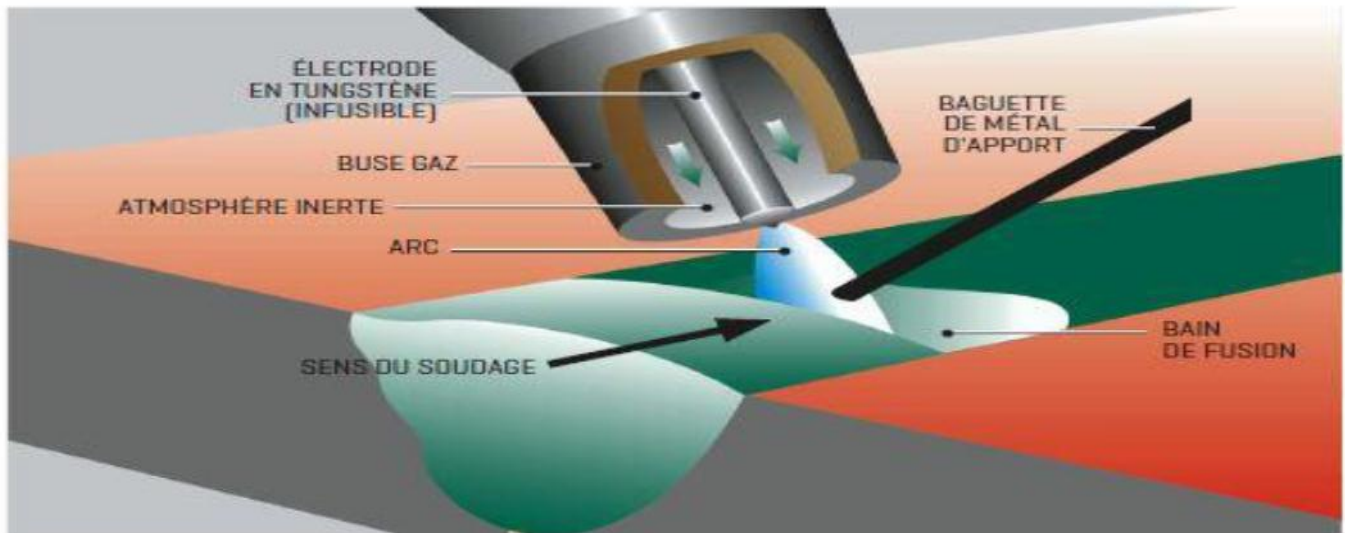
Soudage TIG (Tungstène Inerte Gaz) [14].
